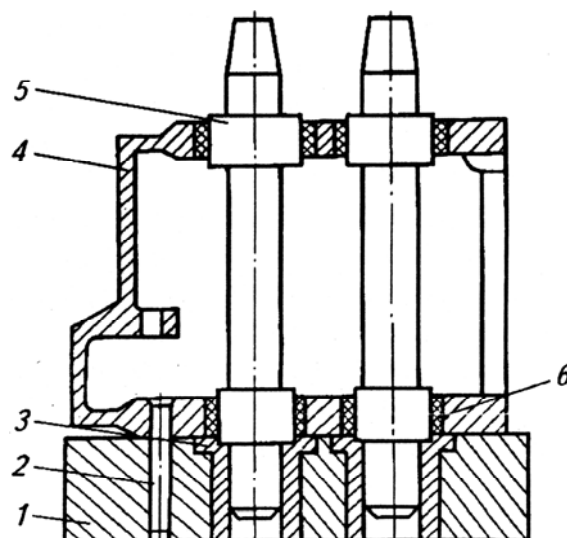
Схема формовки посадочных мест подшипников корпуса коробки передач:
